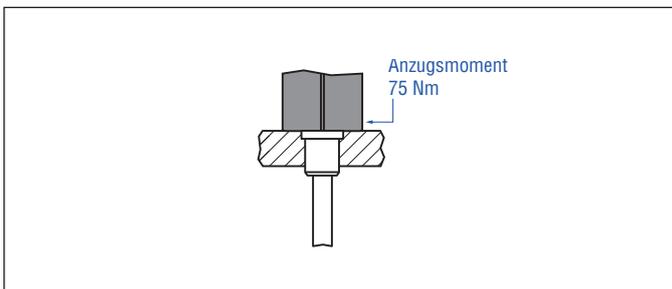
Einbaubeispiel für Gewindeflansch »F«, »M«, »S«, »W«
